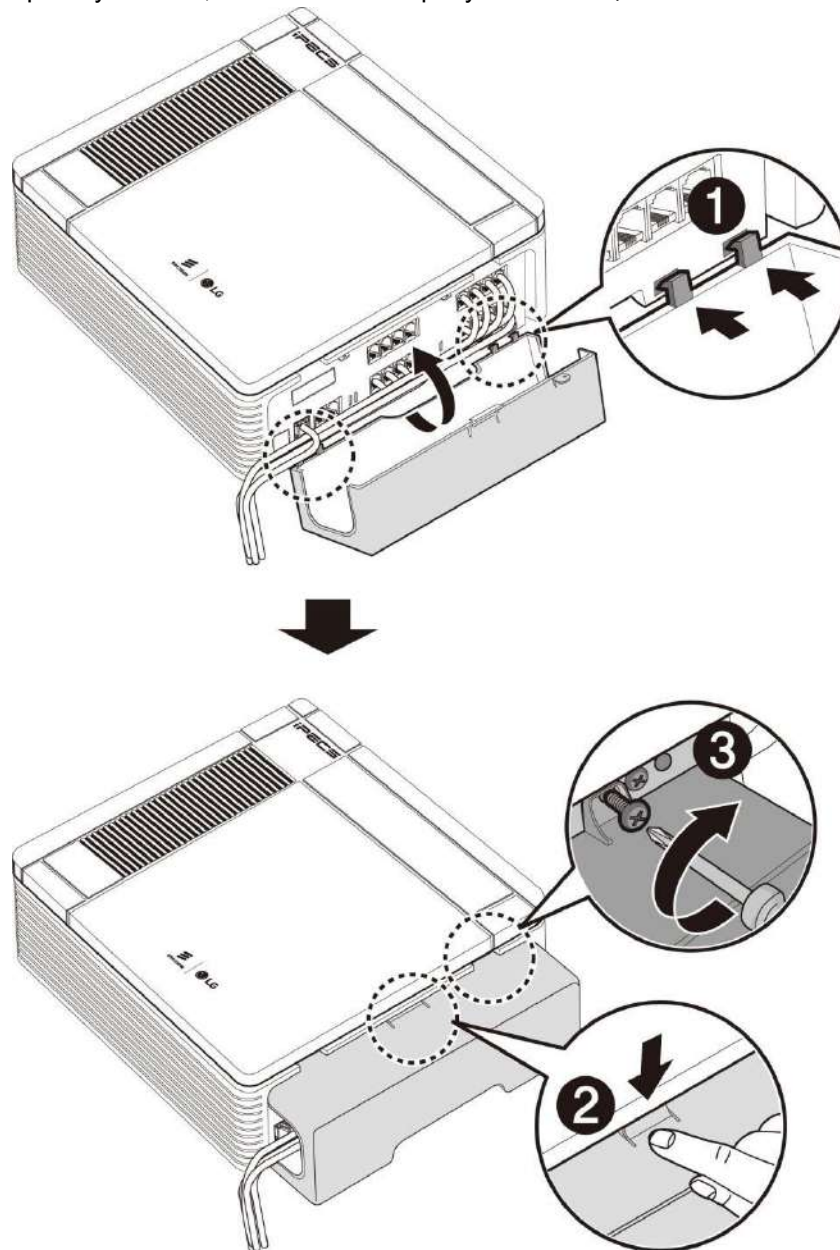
Снятие и установка кабельного кожуха
